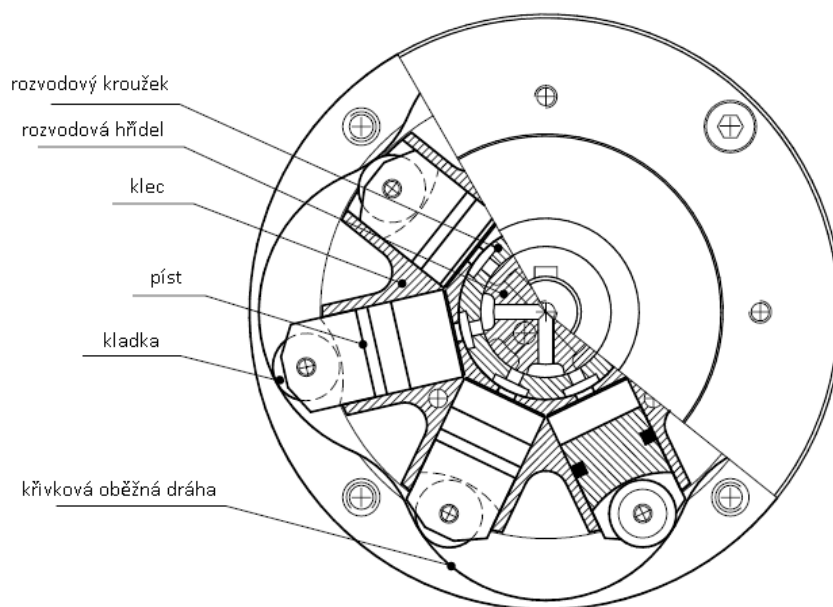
Schéma pneumatického motoru s kulisovým mechanismem[10]
